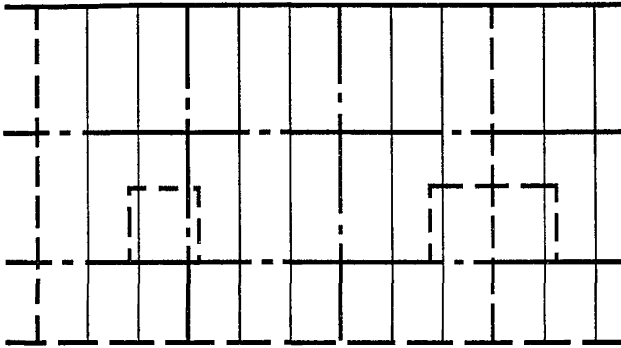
Типовая схема палубного перекрытия с промежуточным карлингсом и усиленными бимсами.
